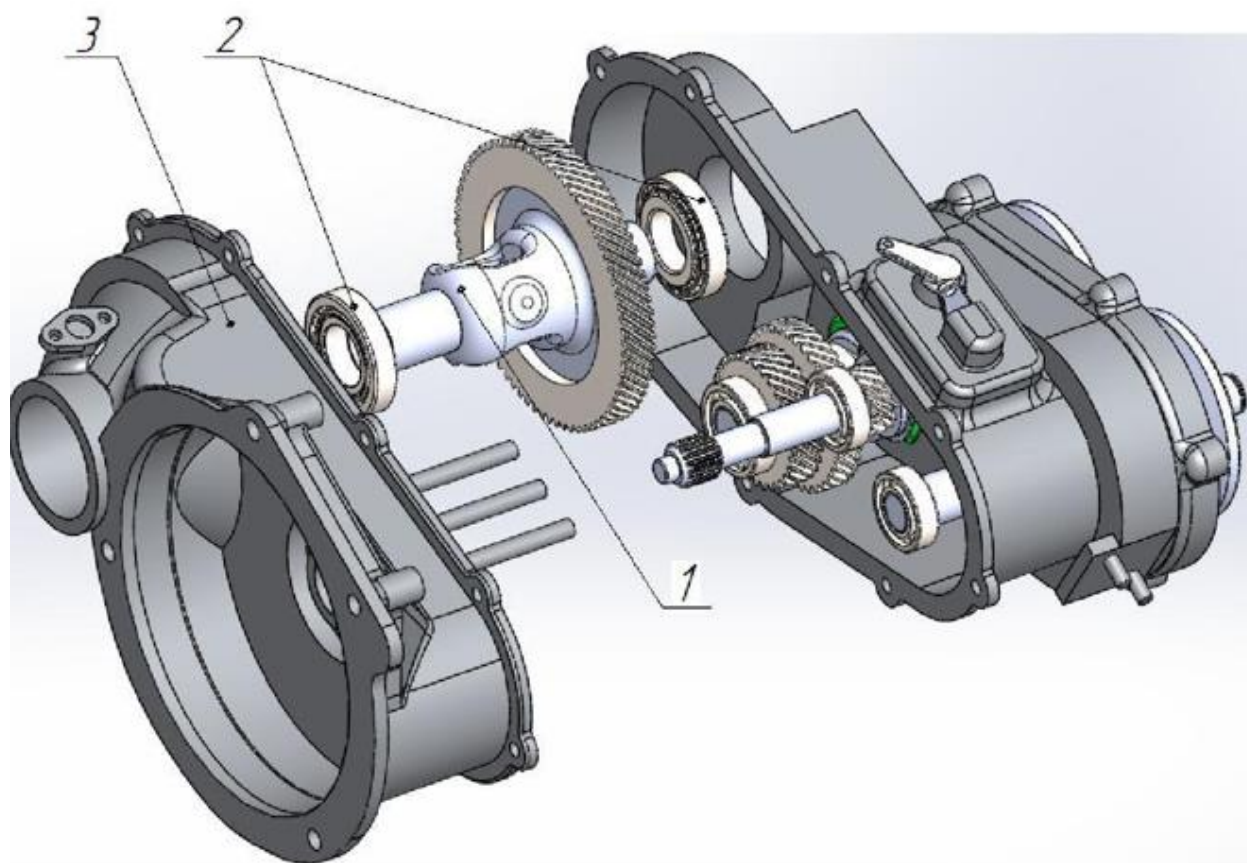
Главная передача и дифференциал: 1 – главная передача и дифференциал; 2 – роликовые подшипники качения; 3 – крышка коробки передач
